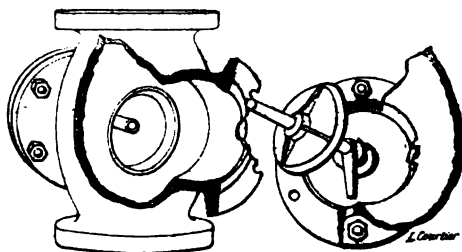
Rupture de la valve V de la chaudière n° 1 (Villefranche).
